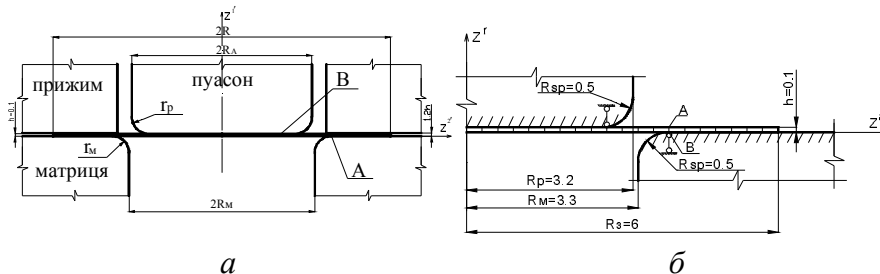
Стенд витяжки круглої пластини в циліндричний стакан (а), розрахункова схема процесу витяжки (б)
